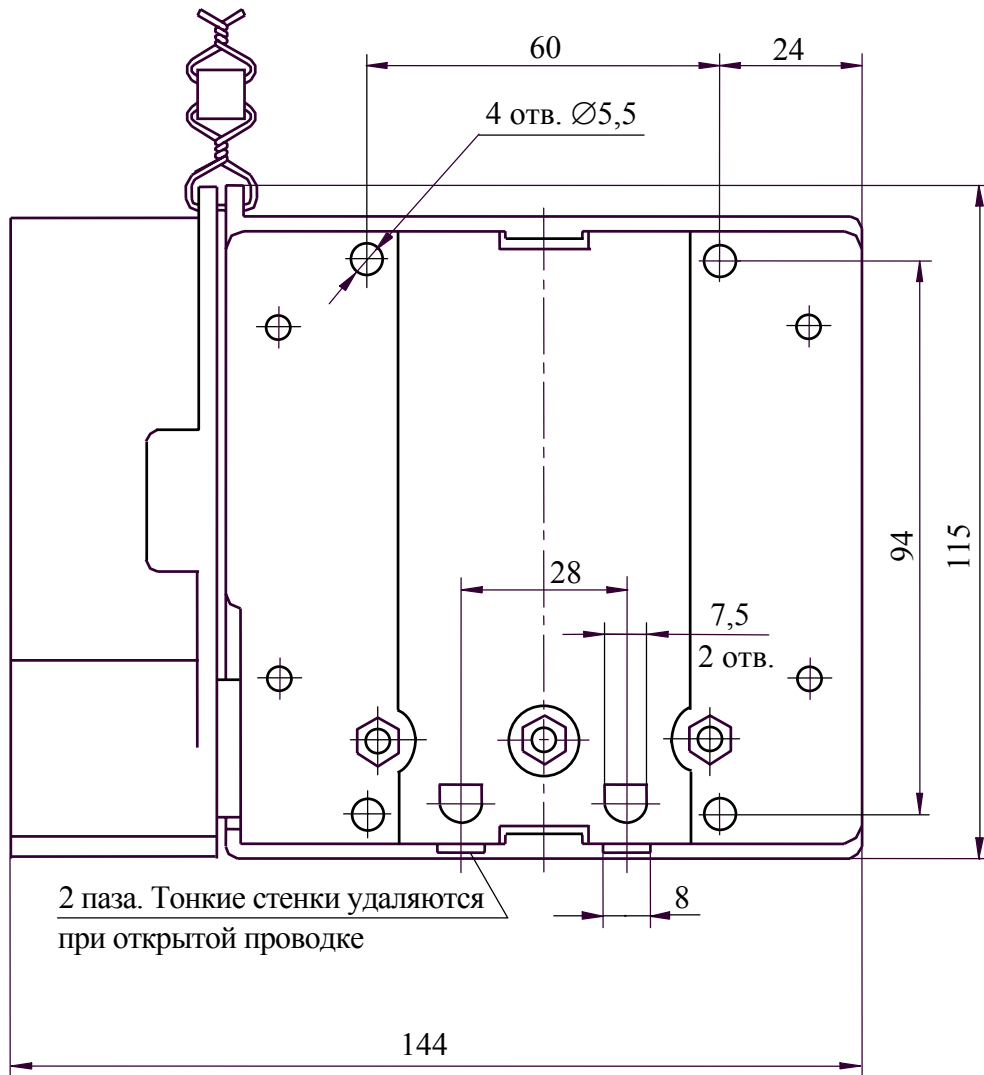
Установочные размеры извещателя ИПР-01Л
